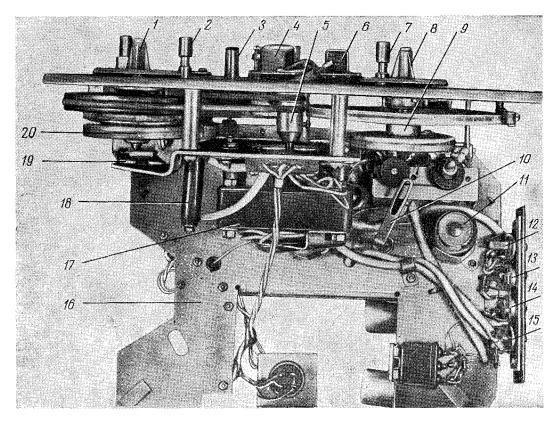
Лентопротяжный механизм (вид сзади) и шасси усилителя (вид сверху).
